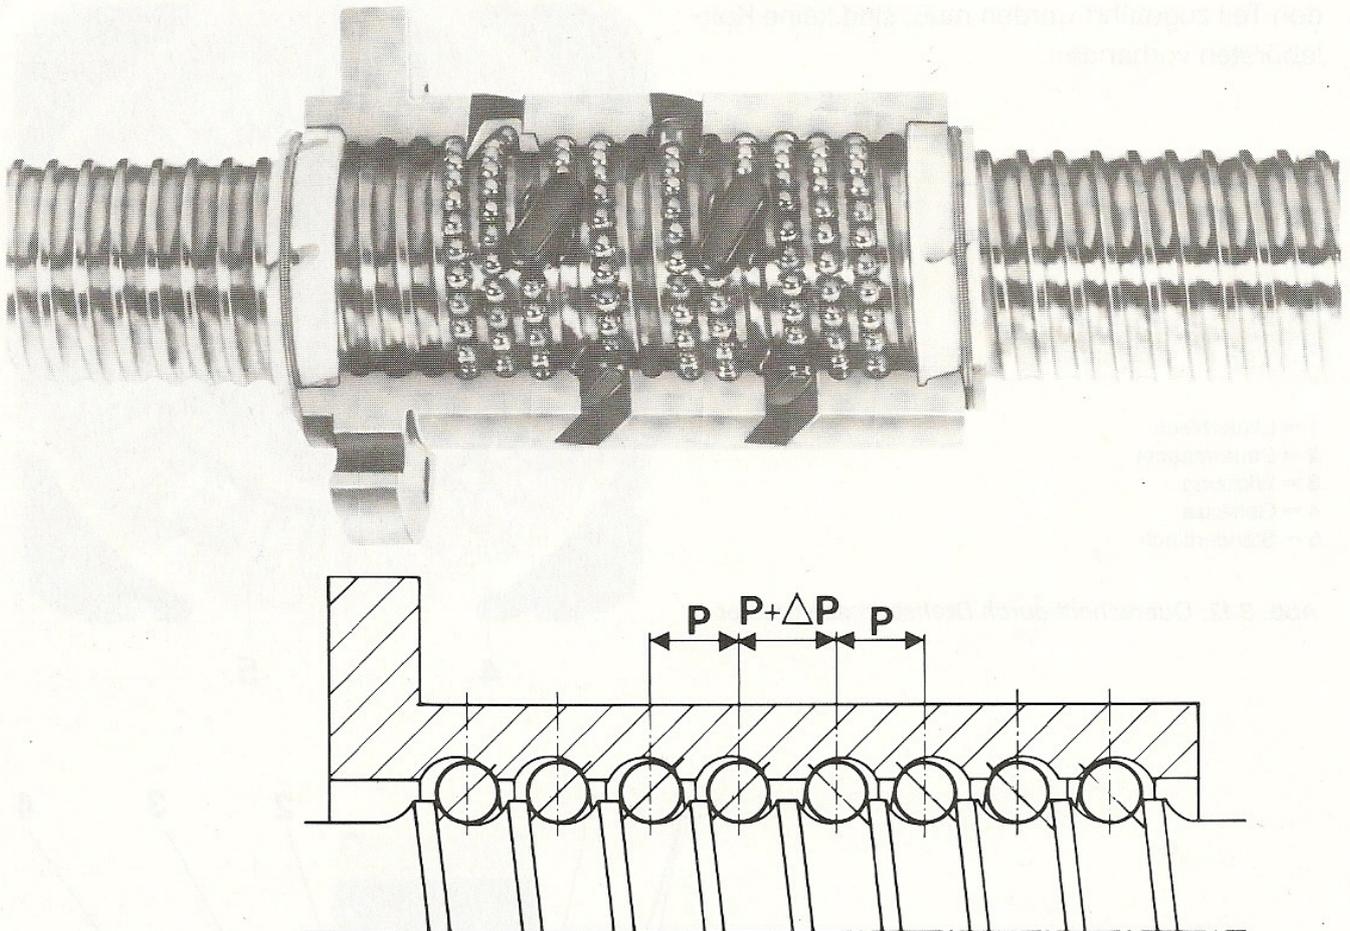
Kugelgewindetrieb mit vorgespannter Einzelmutter
